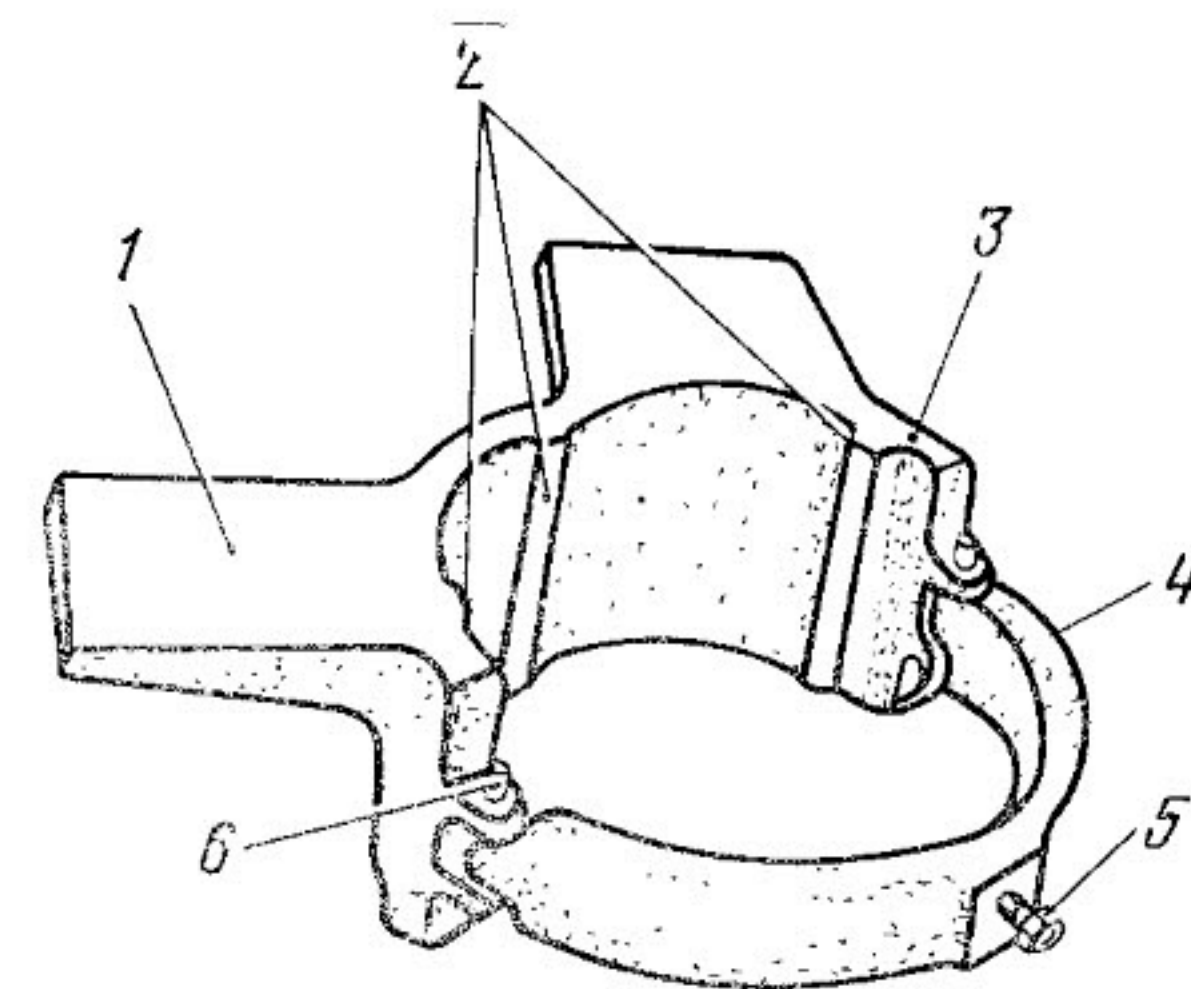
Приспособление для проверки установки редуктора Р-7:
